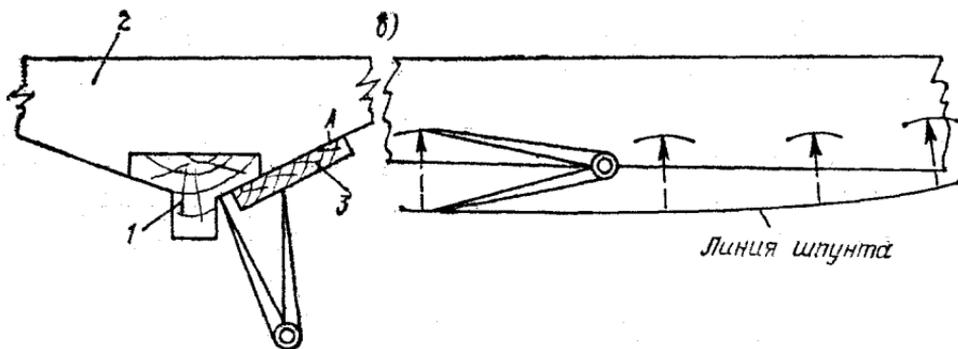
Разметка шпунтового пояса: а — поперечное сечение; б — вид сбоку. 1 — плита; 2 — лекало; 3 — шпунтовый пояс; А — отметка ширины пояса на лекале.
